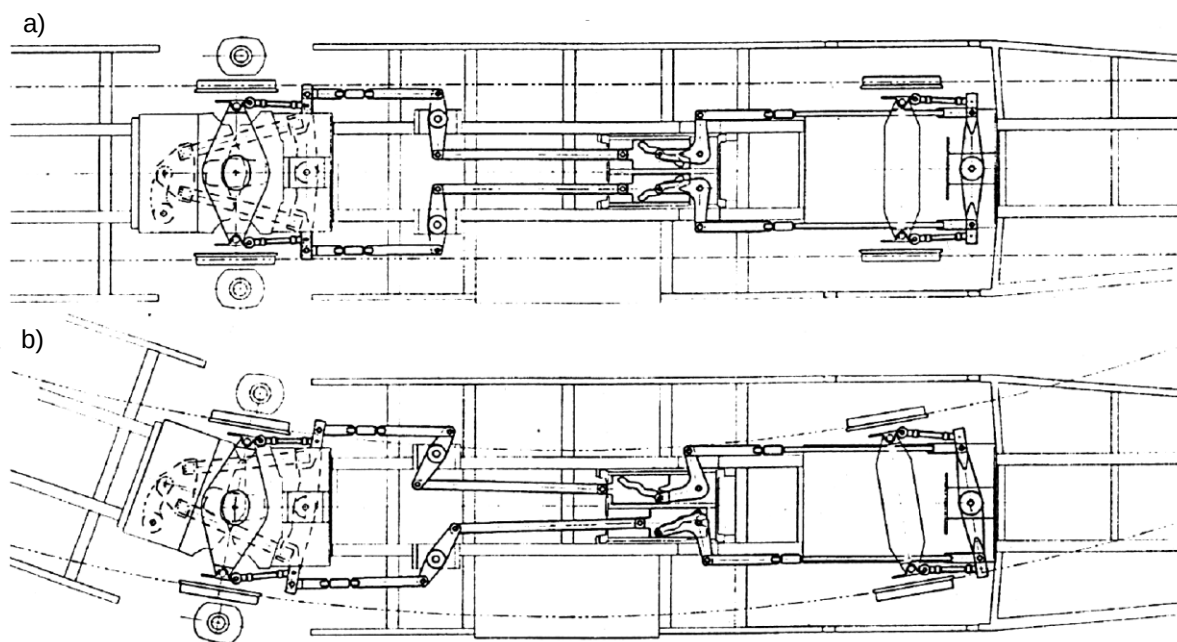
Widok konfiguracji tramwaju Siemens ULF [59].
